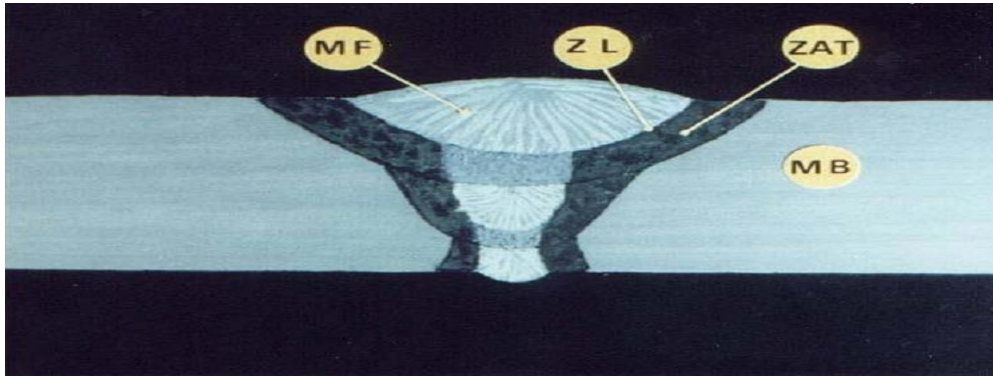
Les différentes zones d'un assemblage soudé.
